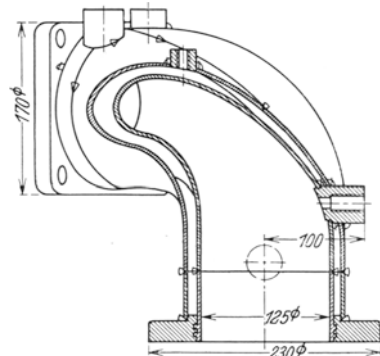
Geschweißter Auspuffstutzen einer Dieselmachine.
